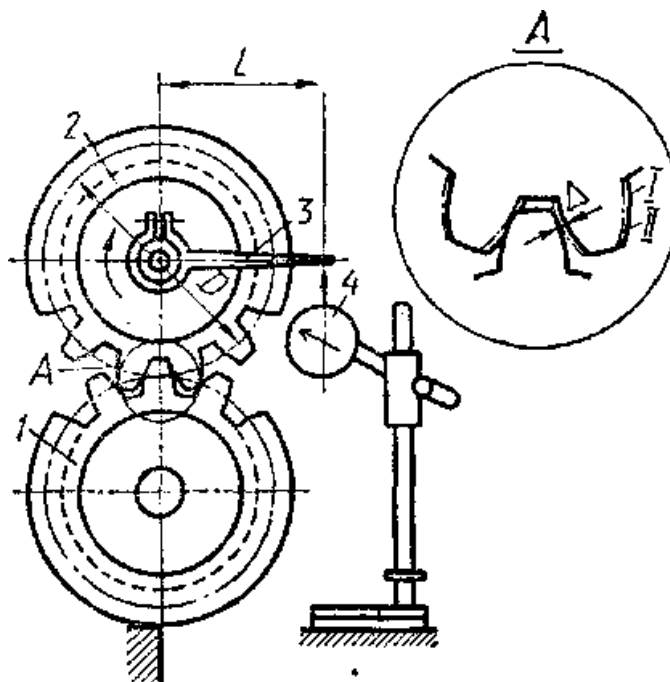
Перевірка бічного зазору в зачепленні циліндричних зубчастих коліс: 1 - нижня шестерня; 2 - зубчасте колесо; 3 - хомутик; 4 - індикатор; I, II - різні відносні положення зубчастого колеса.
